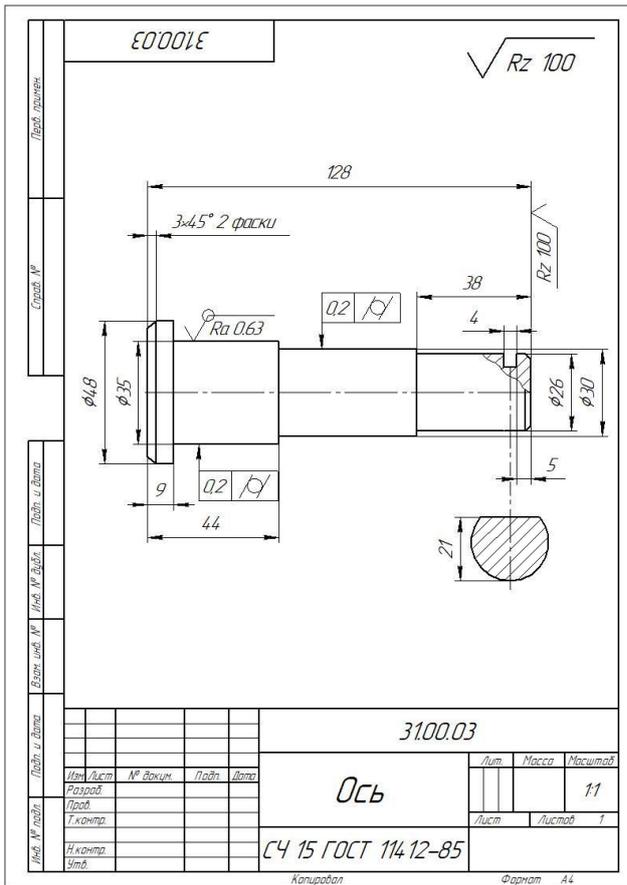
Образец выполнения задания КГ 3.3: рабочий чертёж
